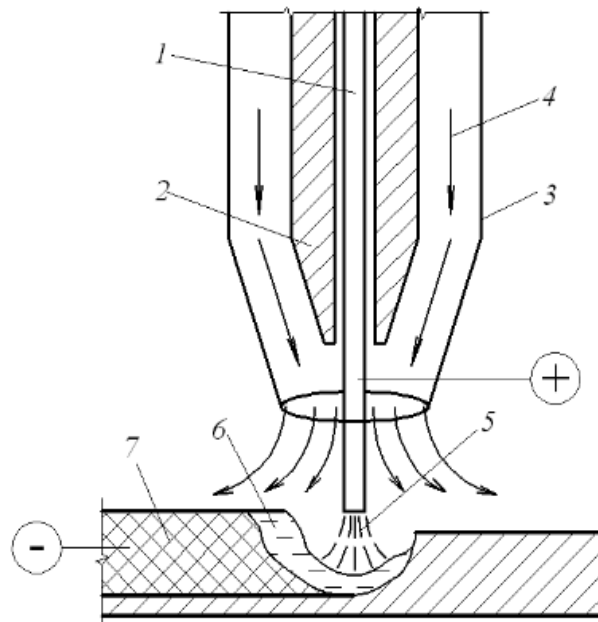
Спосіб зварювання в середовищі CO_2 : 1 – зварювальний дріт; 2 – струмопровідний мундштук; 3 – сопло; 4 – струмінь захисного газу; 5 – зварювальна дуга; 6 – зварювальна ванна; 7 – шов
